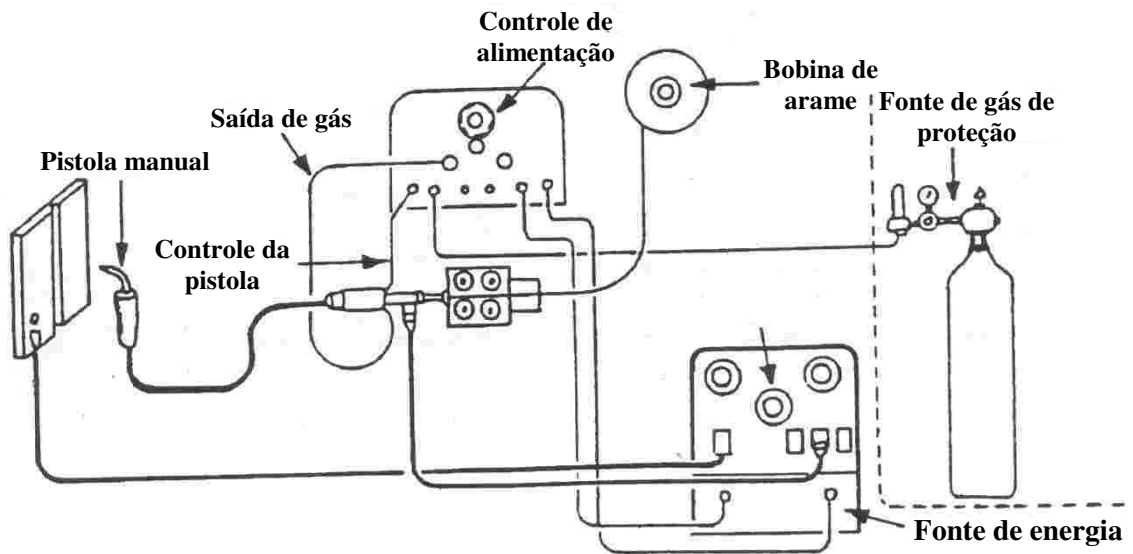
Equipamento básico de soldagem Arame Tubular (FBTS, 1999)
